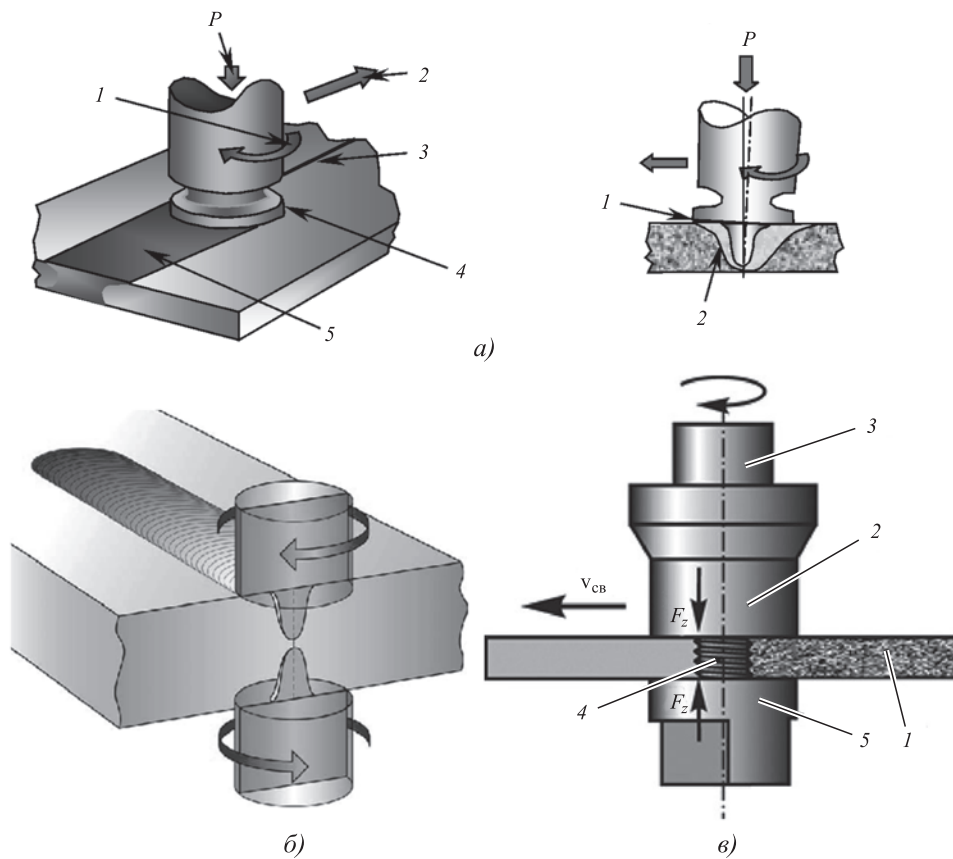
Исследуемые схемы процесса сварки трением с перемешиванием:
